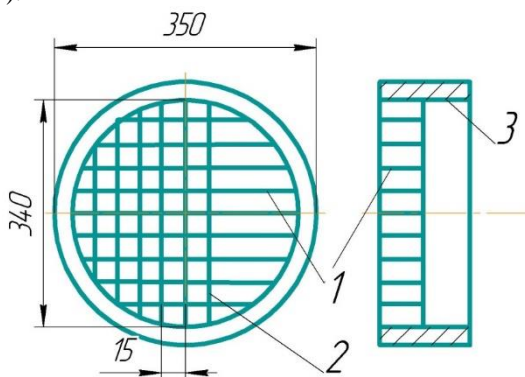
Матрица с бесфасковыми лезвиями: 1 – первый пакет, с горизонтальным расположением лезвий; 2 – второй пакет, с вертикальным расположением лезвий; 3 – обечайка для натяжки ножей.
